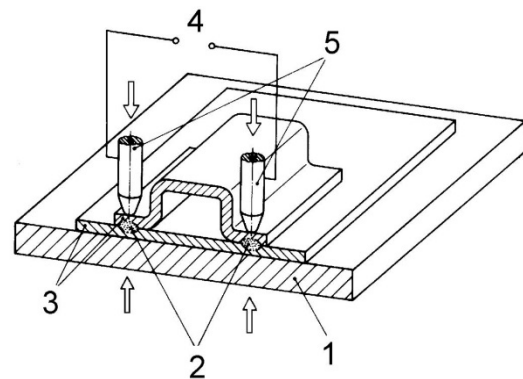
Einseitiges Punktschweißen [11]
